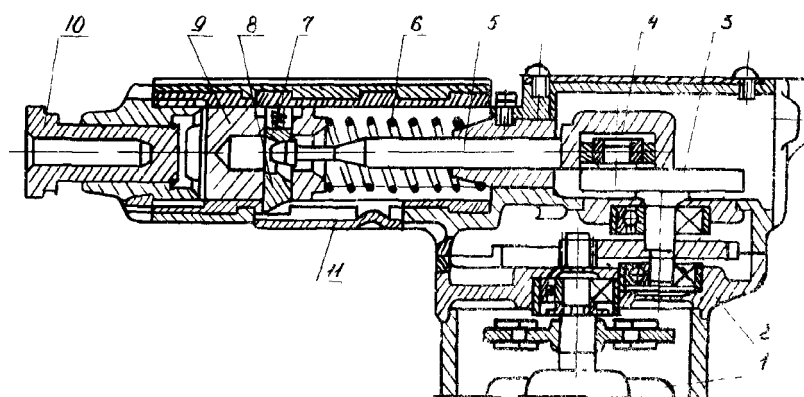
Конструктивная схема клепального молотка с электромеханическим приводом
